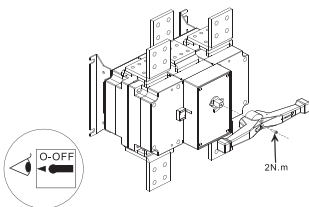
а – Монтаж ручки на корпус рубильников 2000-3150 А
